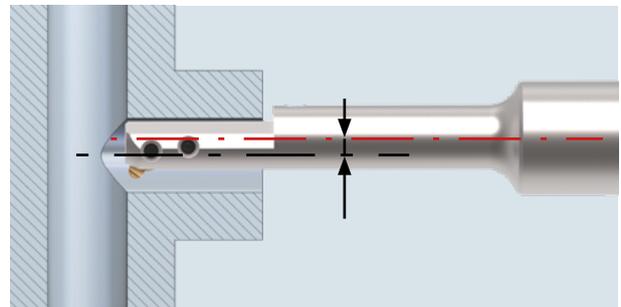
Die Entgratung des T-Stücks erfolgt durch die Querbohrung.
